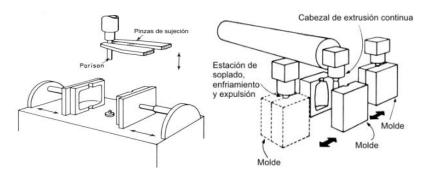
Proceso continuo a) (derecha) Moldes móviles b) (izquierda) Moldes fijos.
